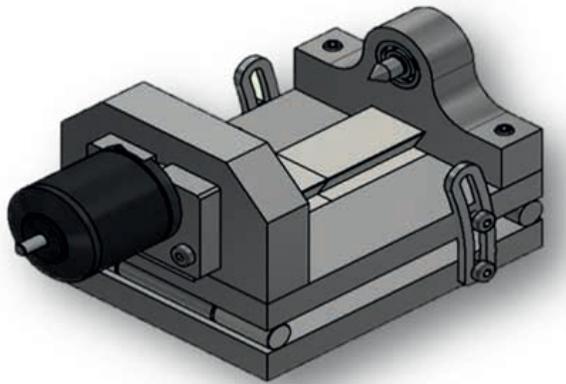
Dispositivo de adaptação de retíficas planas para usinagem de peças cilíndricas
